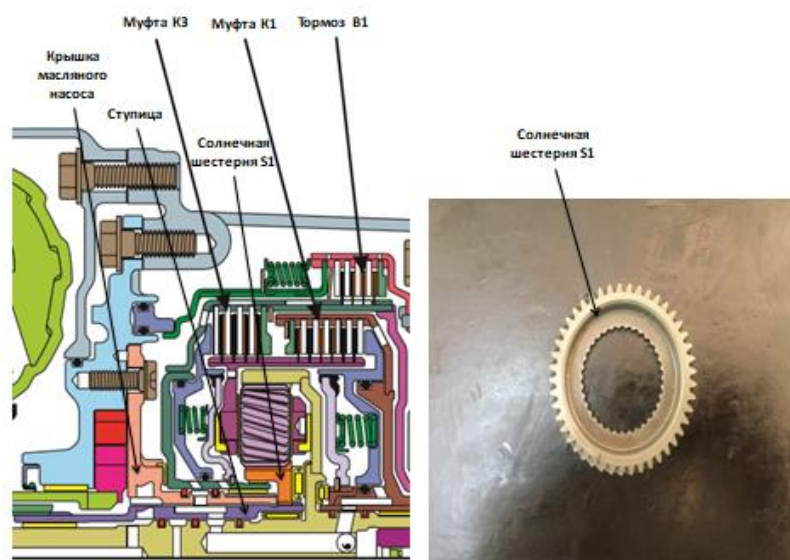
Устройство солнечной шестерни S1 и расположение ее в картере
